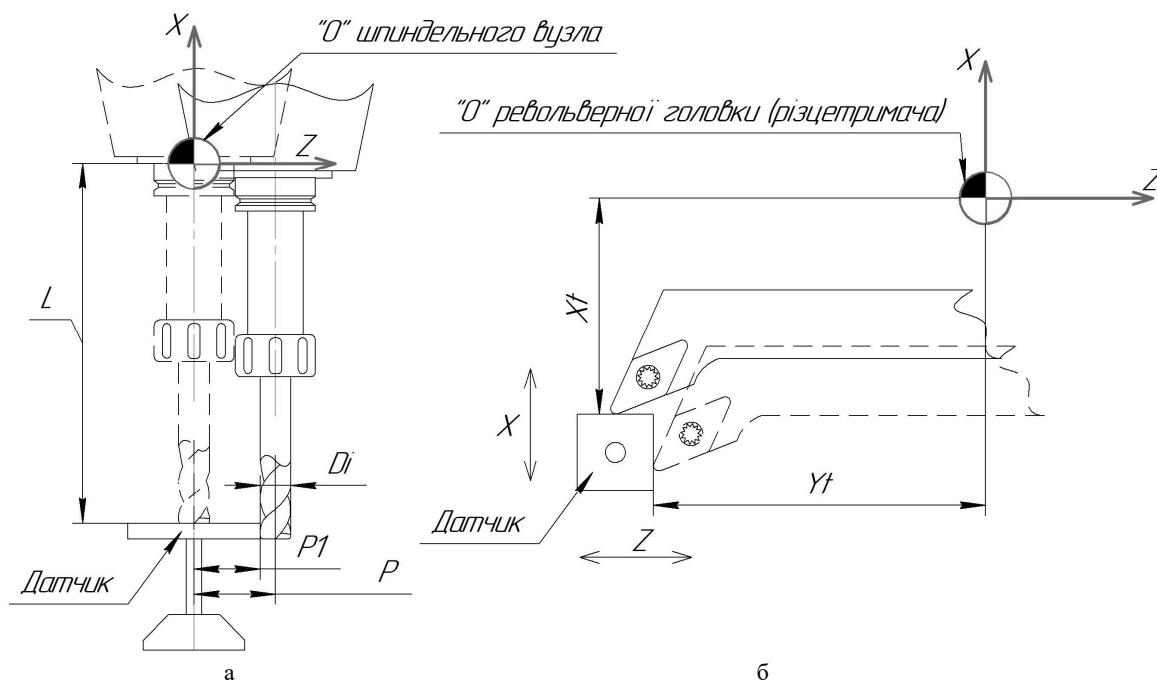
Схеми вимірювання інструменту контактними вимірювальними приладами на верстатах фрезерної групи (а) і токарної групи (б)
